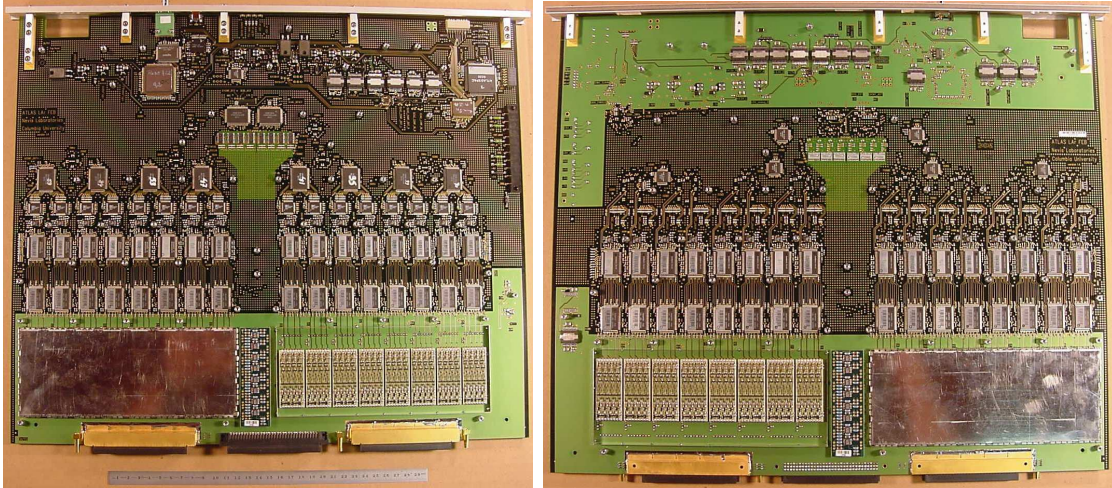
Photographies [16] des faces avant (gauche) et arrière (droite) des cartes d'acquisition FEB.
